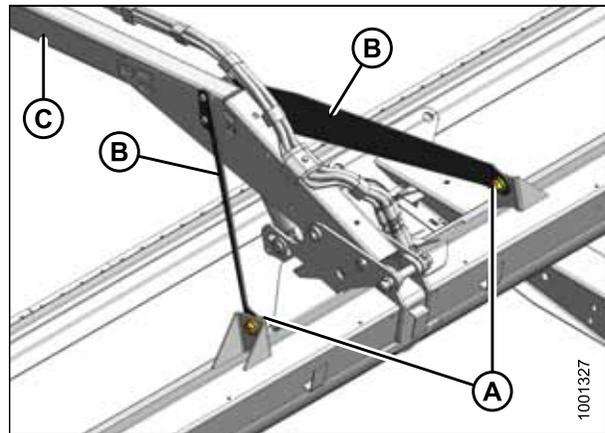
Центральный опорный рычаг подбирающего мотовила
